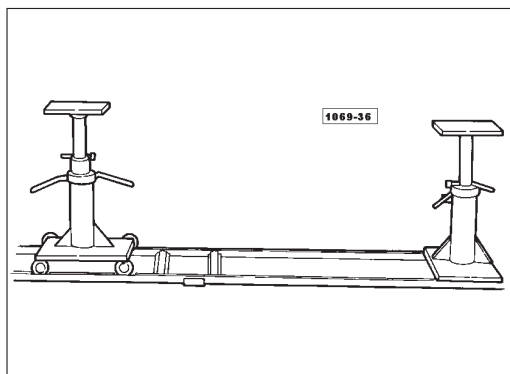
Outil 5.9030.002.0 pour démontage de la boîte de vitesses.-
